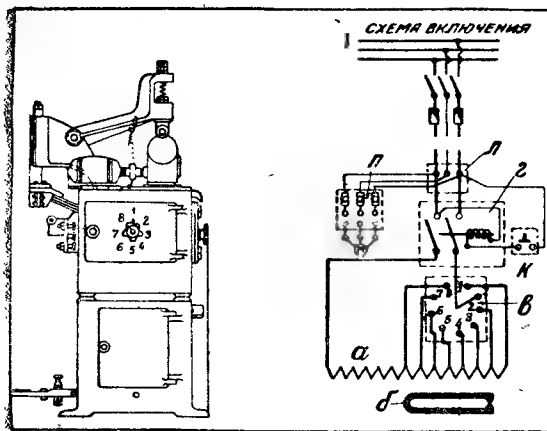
Сварочная машина типа АТА-40-9 и схема ее включения
